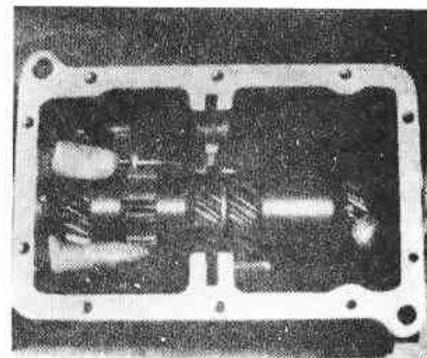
Стопорное кольцо крепления ведущего вала коробки передач типа С (Разд. 7)
